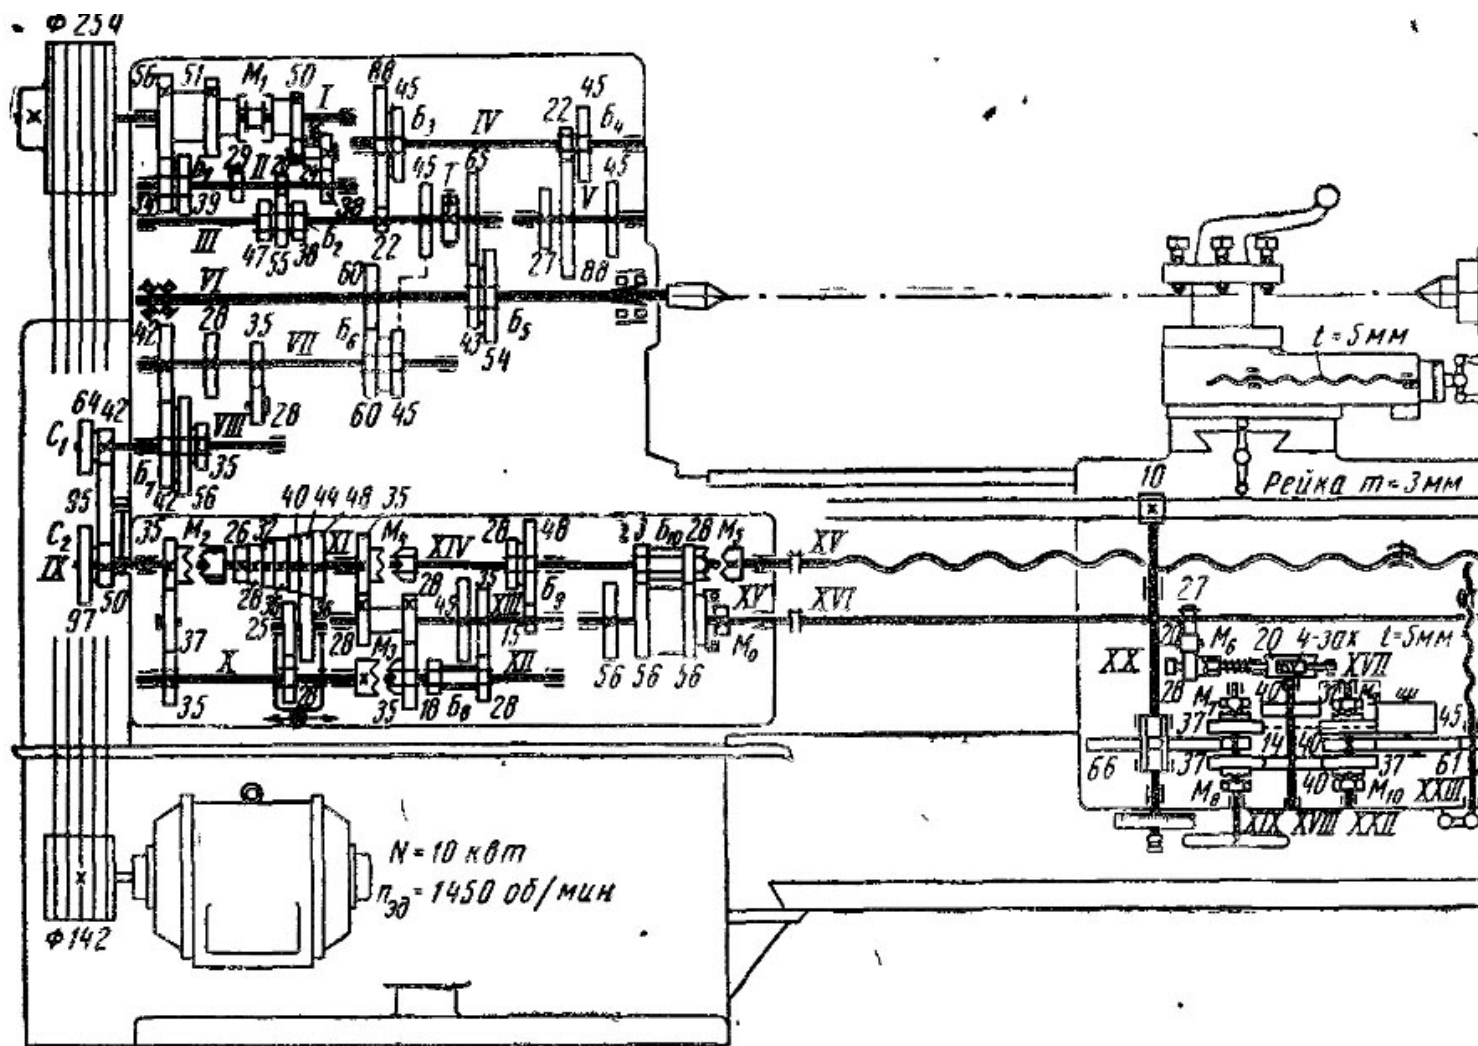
Кинематическая схема токарно-винторезного станка модели 1К62
